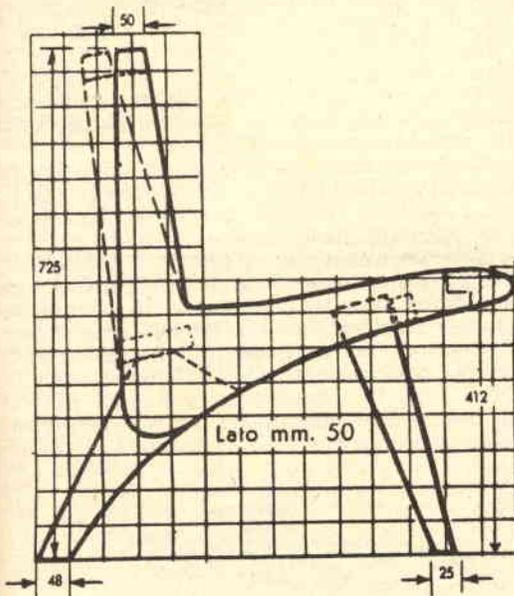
Fabbisogno: Fianchi e gambe: in legno compensato dello spessore di mm. 20 o mm. 10 in doppio; Traversa posteriore: in legno abete mm. 25 x 100 x 400; Traversa intermedia: in legno abete mm. 225 x 40 x 400; Traversa superiore: in legno abete mm. 40 x 55 x 400; Traversa anteriore: in legno abete mm. 50 x 100 x 440.
